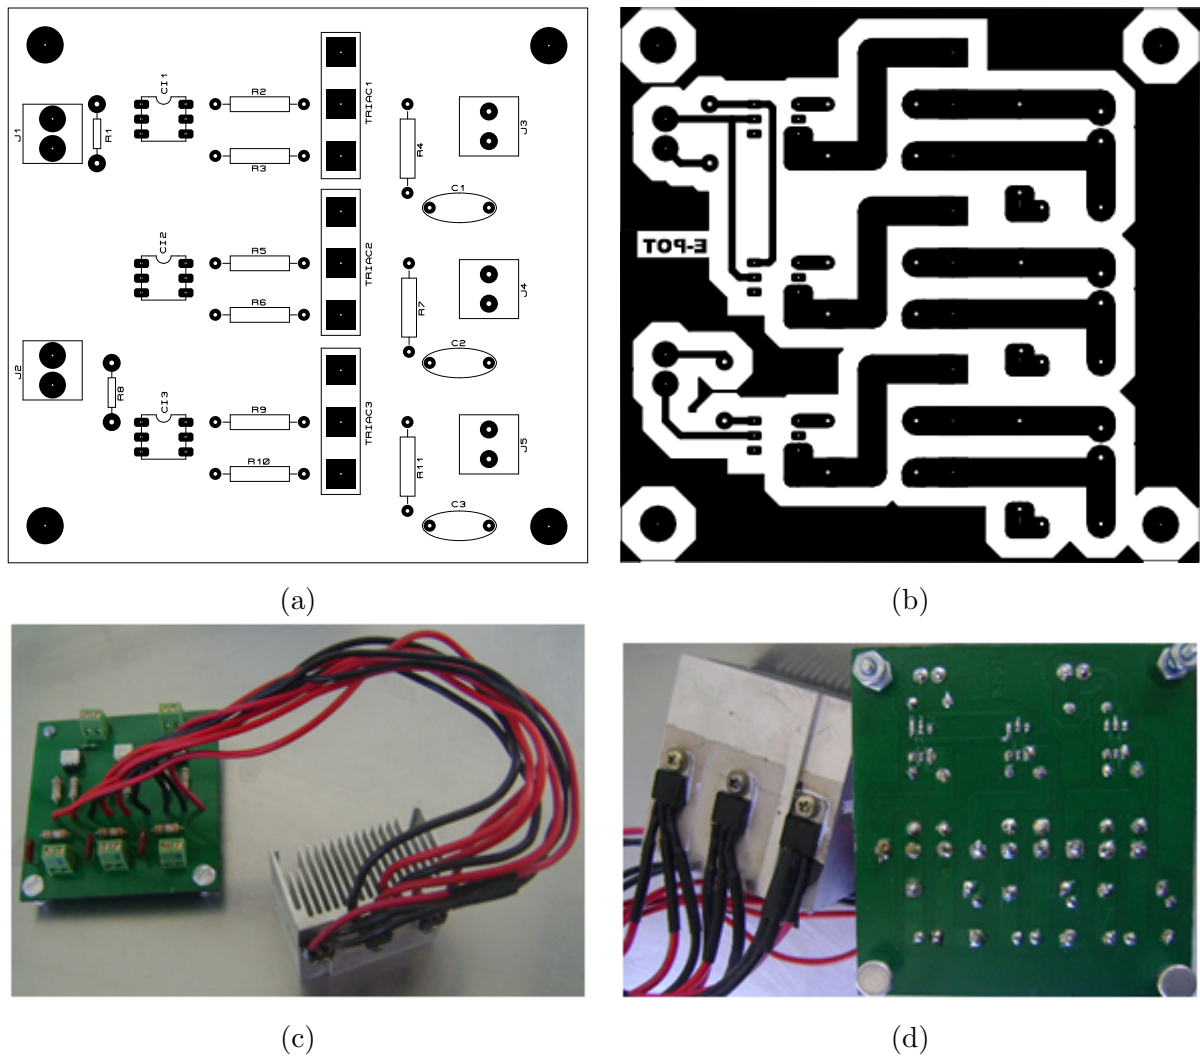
(a) Vista Superior del PCB. (b) Vista Inferior del PCB. (c) Vista Superior del PCB real. (d) Vista Inferior del PCB real.
